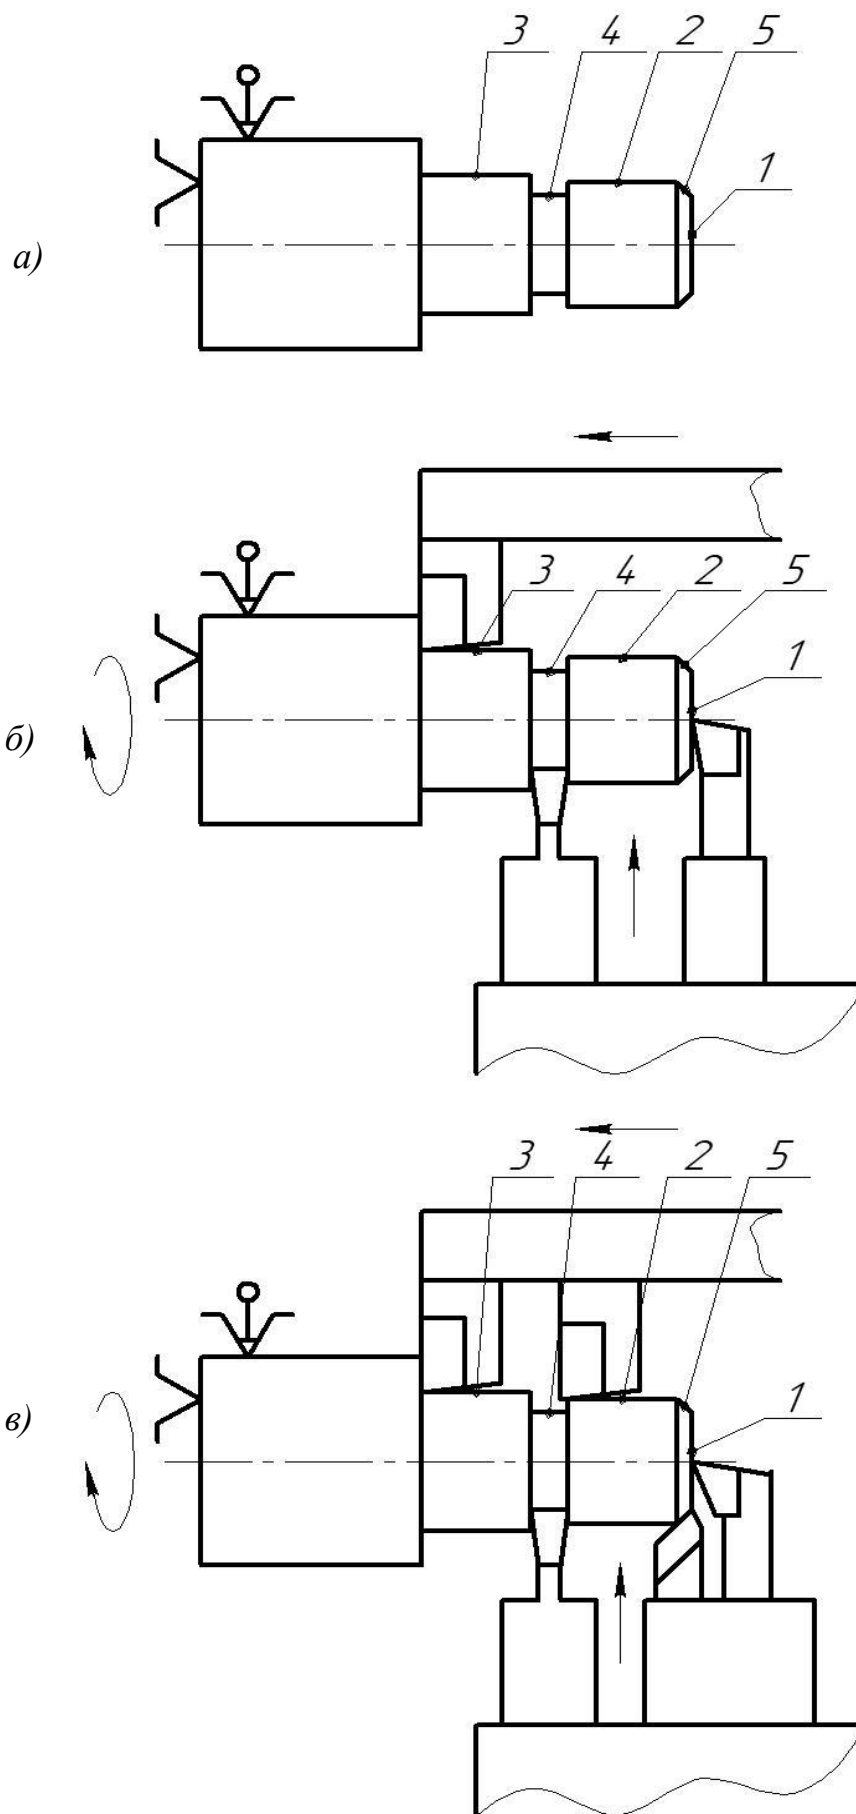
Варіанти багатоінструментальної обробки валу
